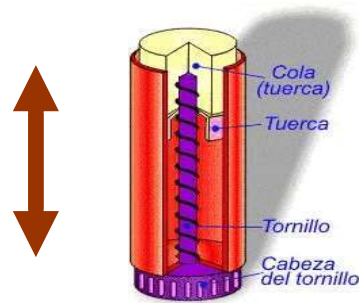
Sistema de movimiento tornillo tuerca
